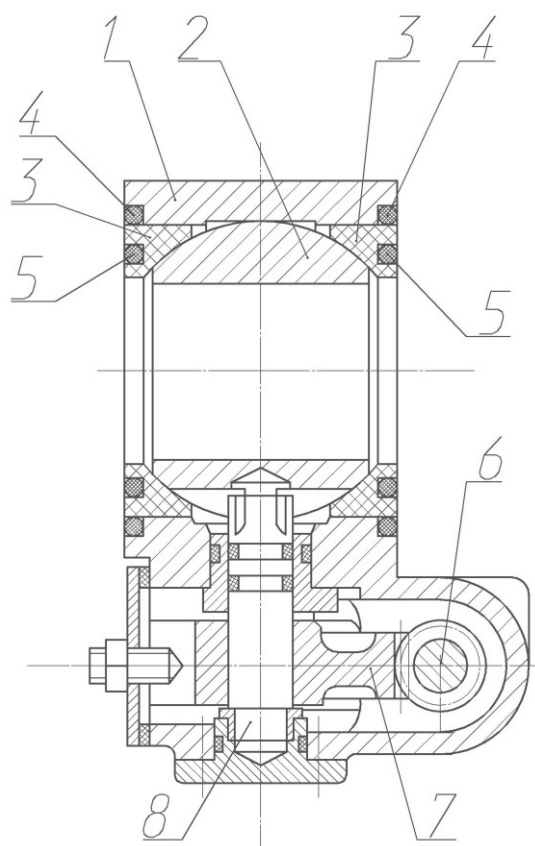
Напорный шаровой кран НЦПВ -20/200: 1 — корпус; 2 — шар; 3 — фторопластовое кольцо; 4, 5 — резиновые уплотнительные кольца; 6 — червяк; 7 — сегмент червячного колеса; 8 — ось
